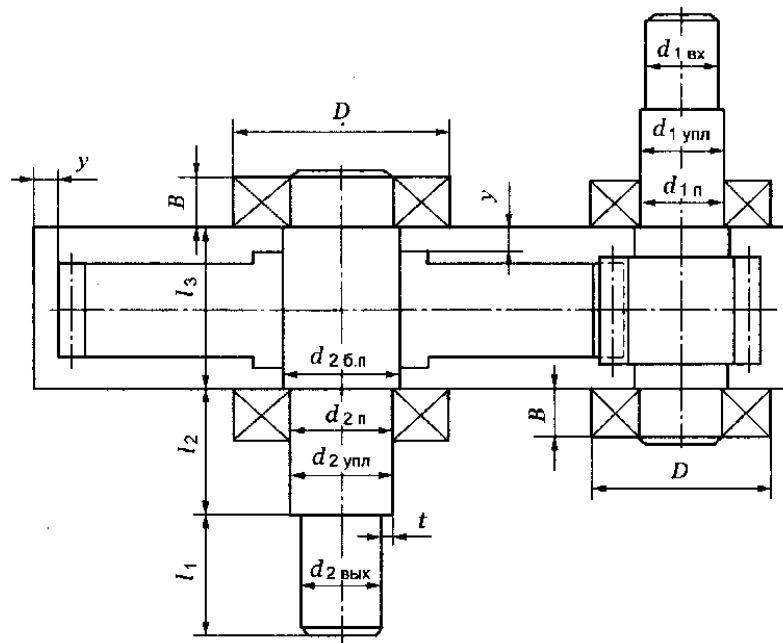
Эскиз цилиндрического редуктора:
